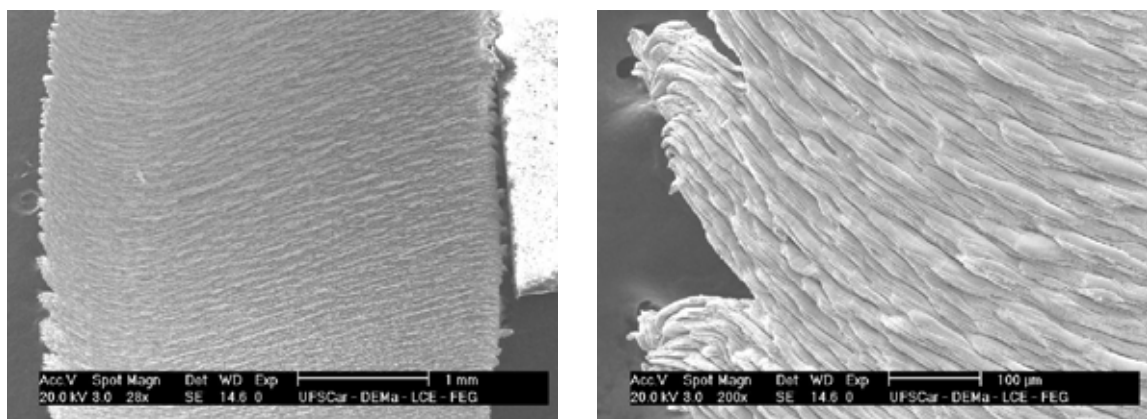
Cavaco extraído da amostra (F) sob a condição de usinagem C2.
